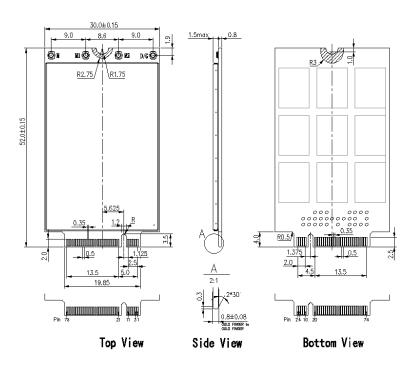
FM650-CN-23/63 结构尺寸(单位: mm)
